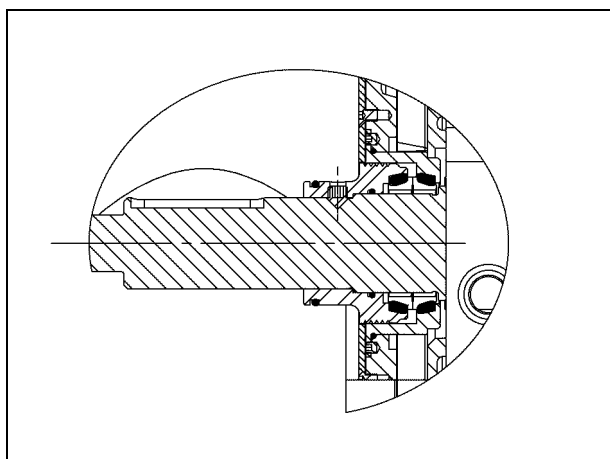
Assemblaggio finale tenute meccaniche.
